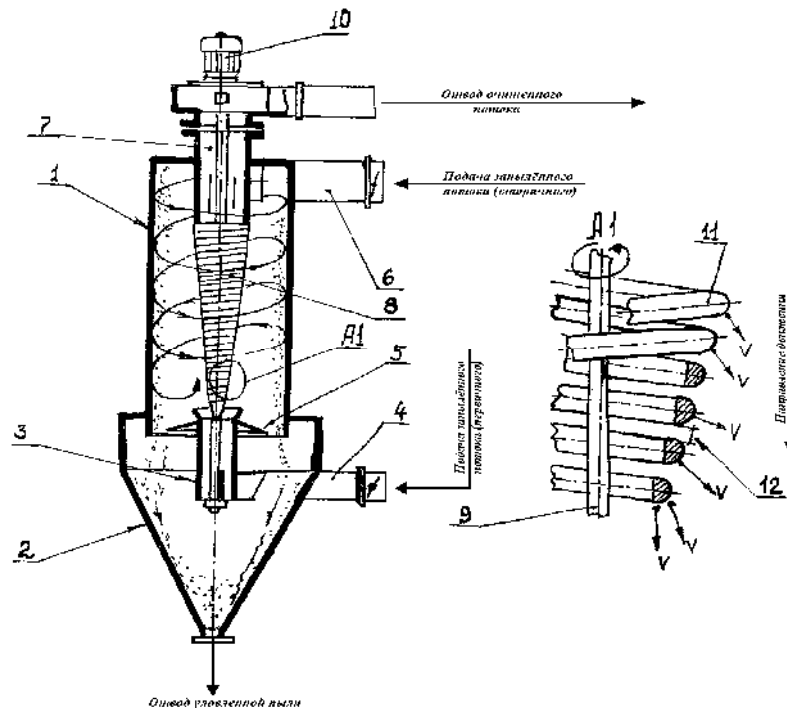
Схема роторно-вихревого пылеуловителя со встречными закрученными потоками: 1 – корпус; 2 – бункер пылесборный; 3 – аксиальный завихритель; 4 – ввод первичного потока; 5 – шайба отбойная; 6 – ввод вторичного потока; 7 – выходной патрубок; 8 – экран роторный; 9 – вал; 10 – привод; 11 – спираль винтовая; 12 – зазор межвитковый
